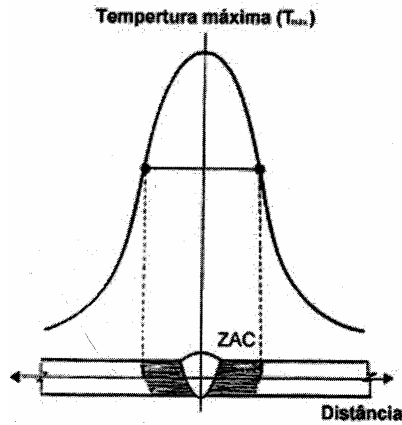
Repartição térmica de uma junta soldada [20].
